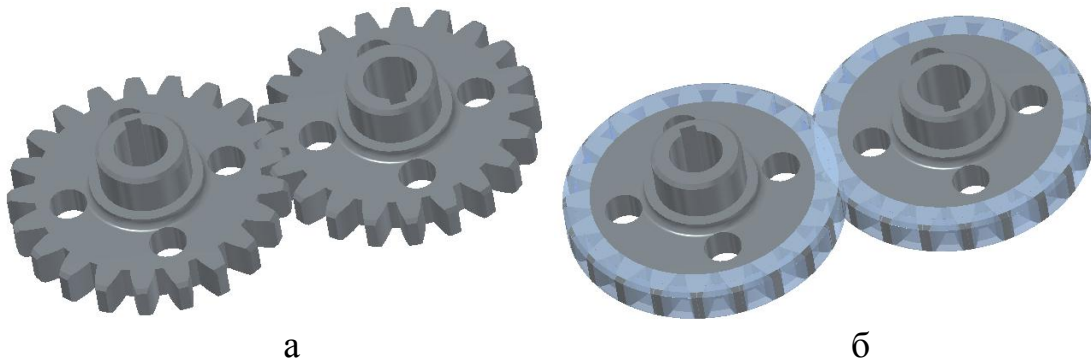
а - 3D-модель циліндричної зубчастої передачі;
